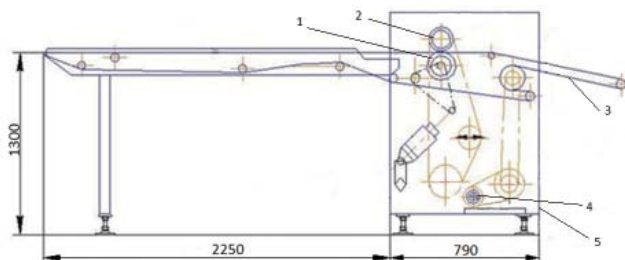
Формувальна машина: 1 — притискний барабан; 2 — штампувальний ротор; 3 — стрічковий конвеєр; 4 — привод; 5 — корпус.
